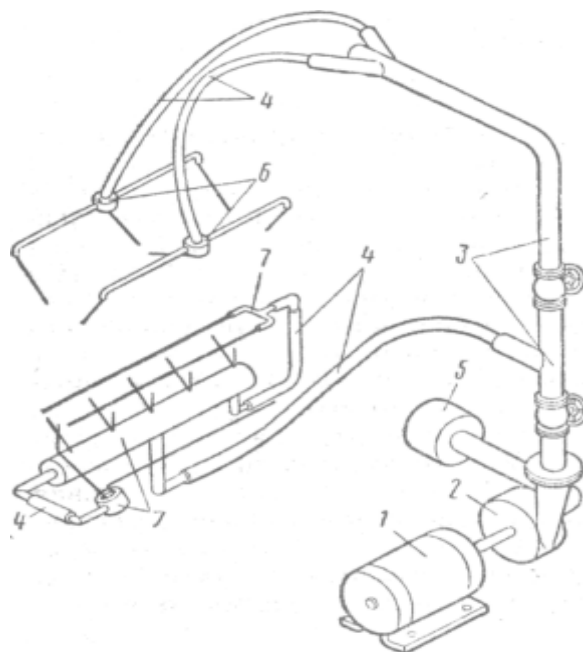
Схема устройства установки для промывки масляных каналов в блоке цилиндров двигателя ЗИЛ-130:
